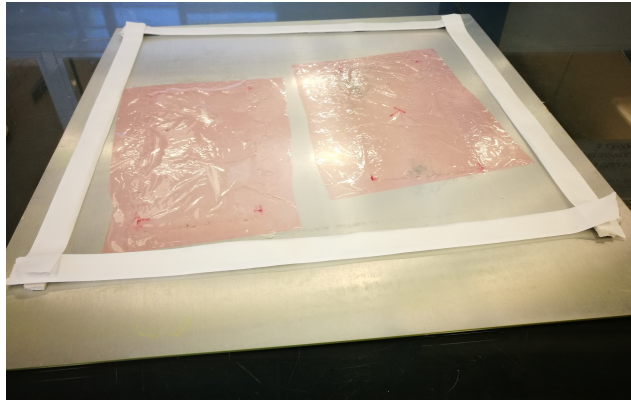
Desmoldeante y sellador perimetral de la placa. Fibra impregnada a 0° (izquierda) y a $\pm 45^\circ$ (derecha).
